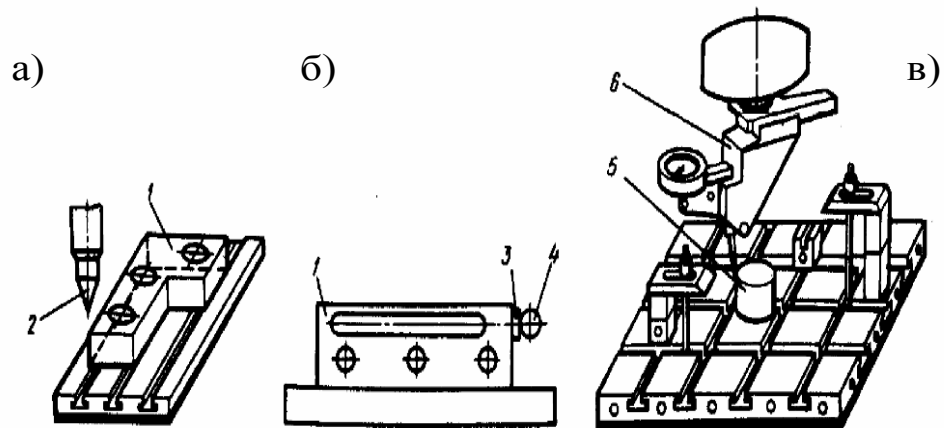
Способы наладки нулевого положения: а - по боковой поверхности с помощью центра; б - по боковой поверхности с помощью контрольной оправки; в - по пальцу с помощью центроискателя; 1- заготовка; 2 – центр; 3 – мерная плитка; 4 – контрольная оправка; 5 – установочный палец; 6 – центроискатель
